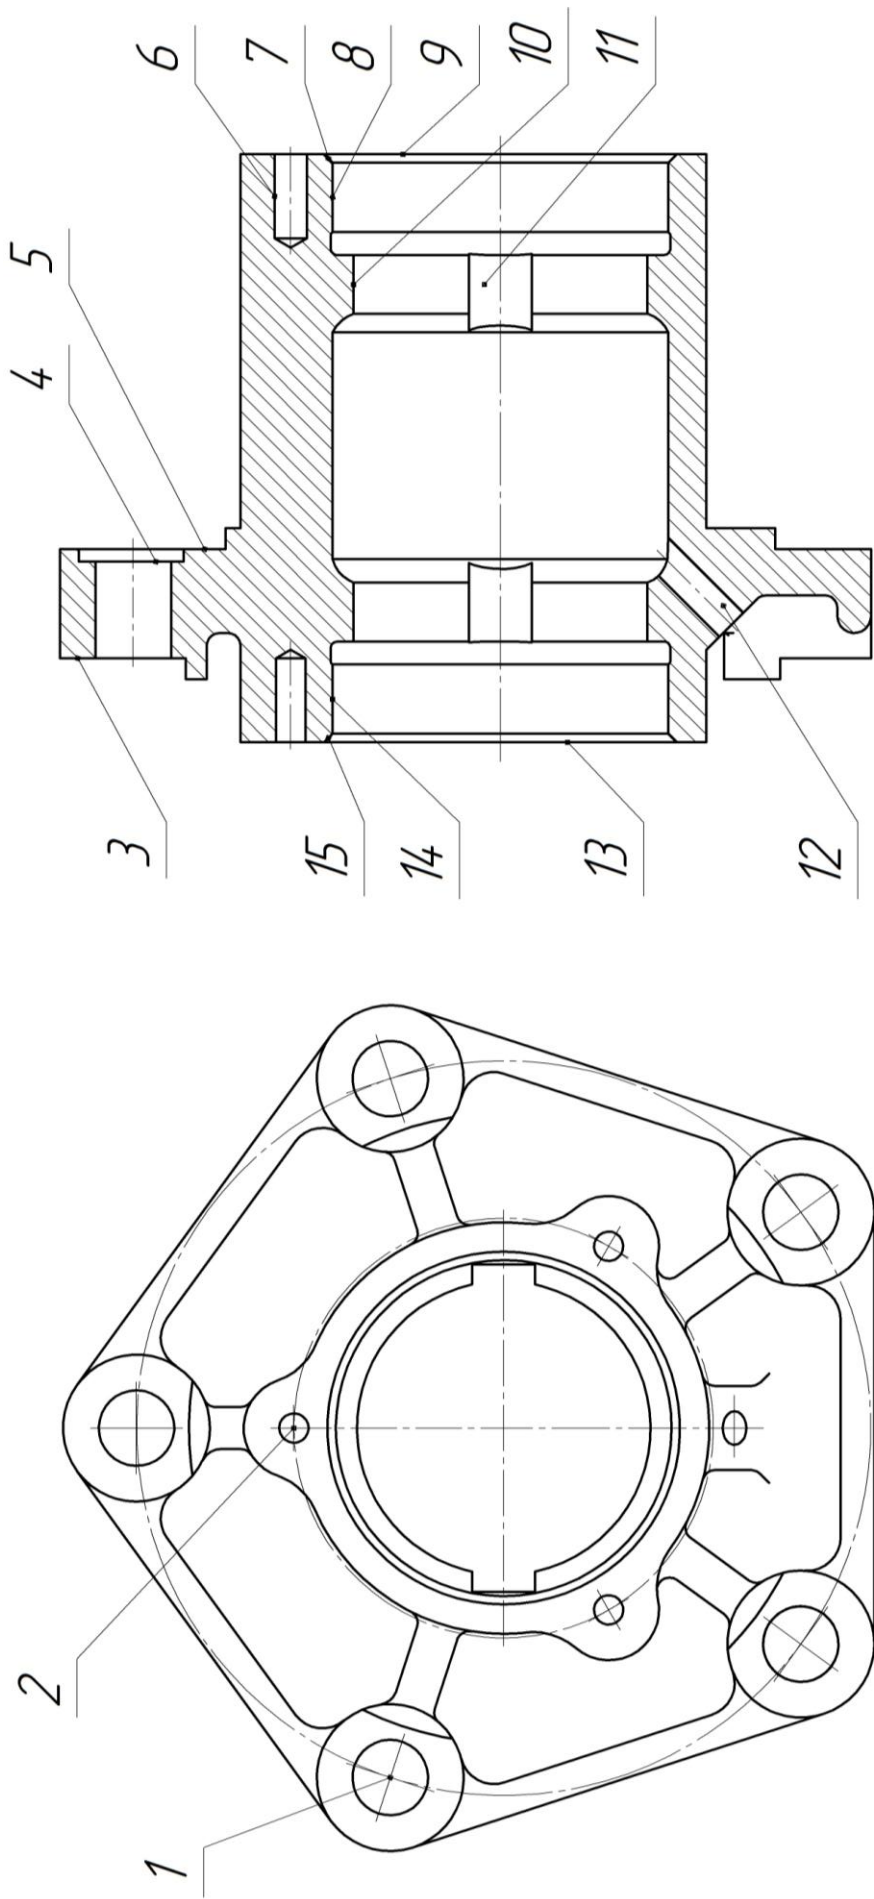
Оброблюємі поверхні деталі маточина
